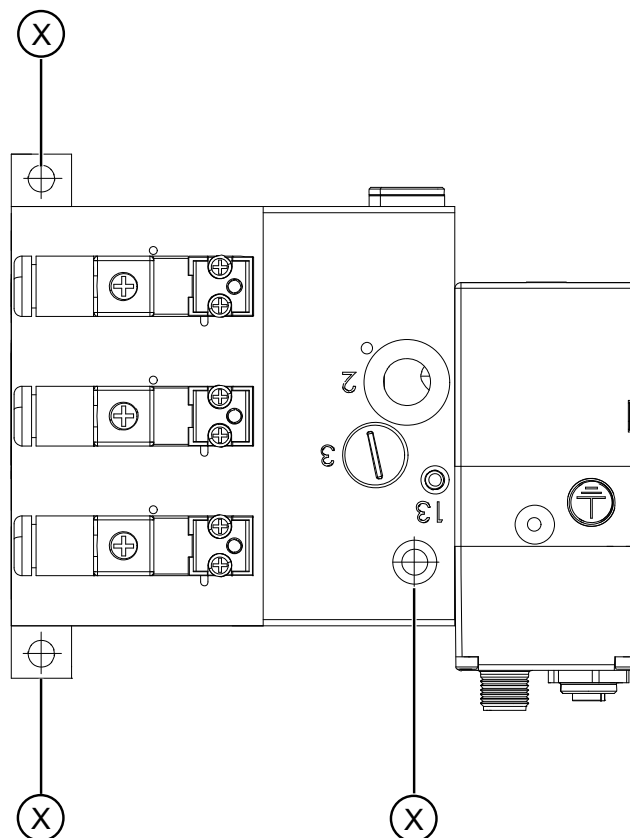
2- und 3-Gas-Standardausführung, Befestigung von oben, Durchgangsbohrung d 6,5
